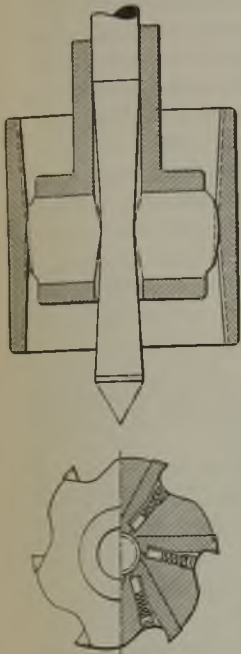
Gewindeschneidkopf für doppelkegeliges Gewinde.
